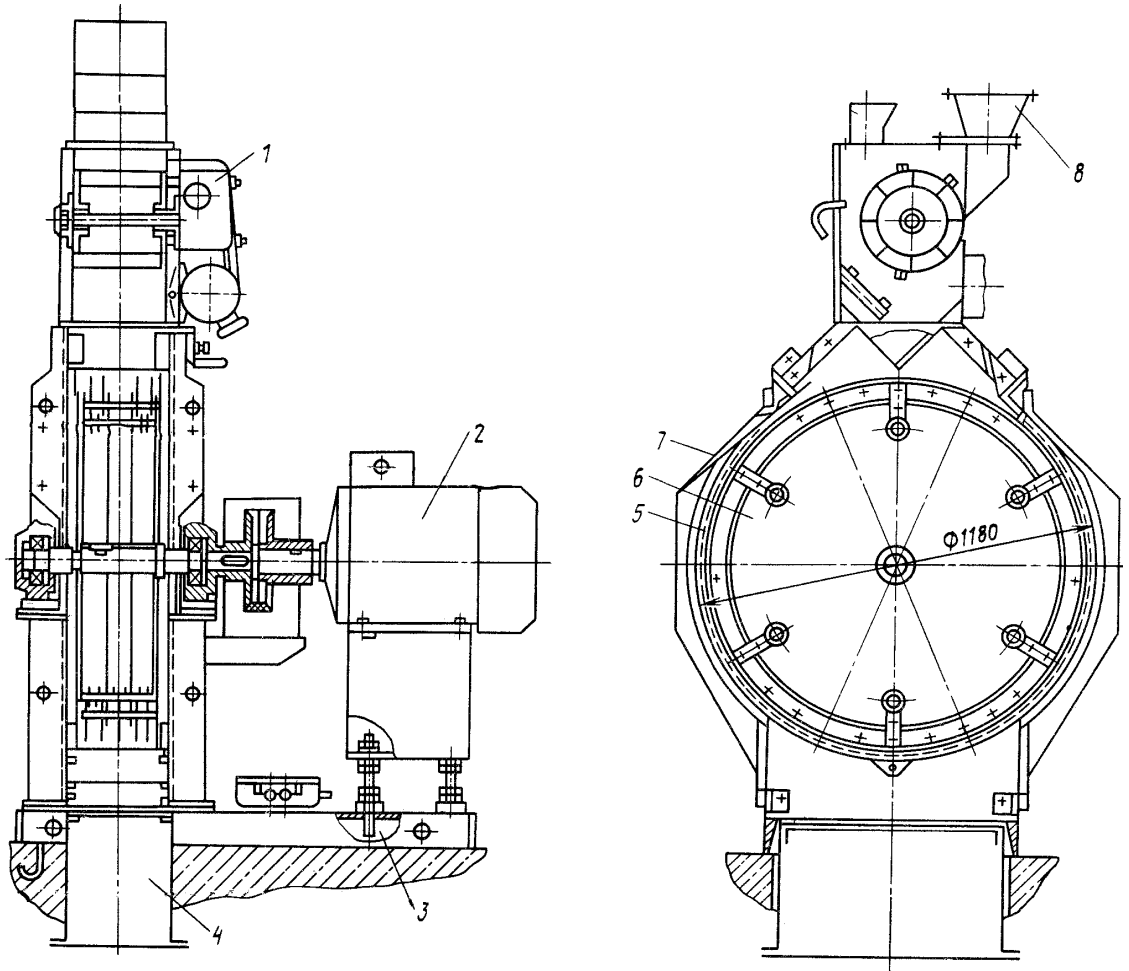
Загальний вид дробарки А1-ДМР-6:
